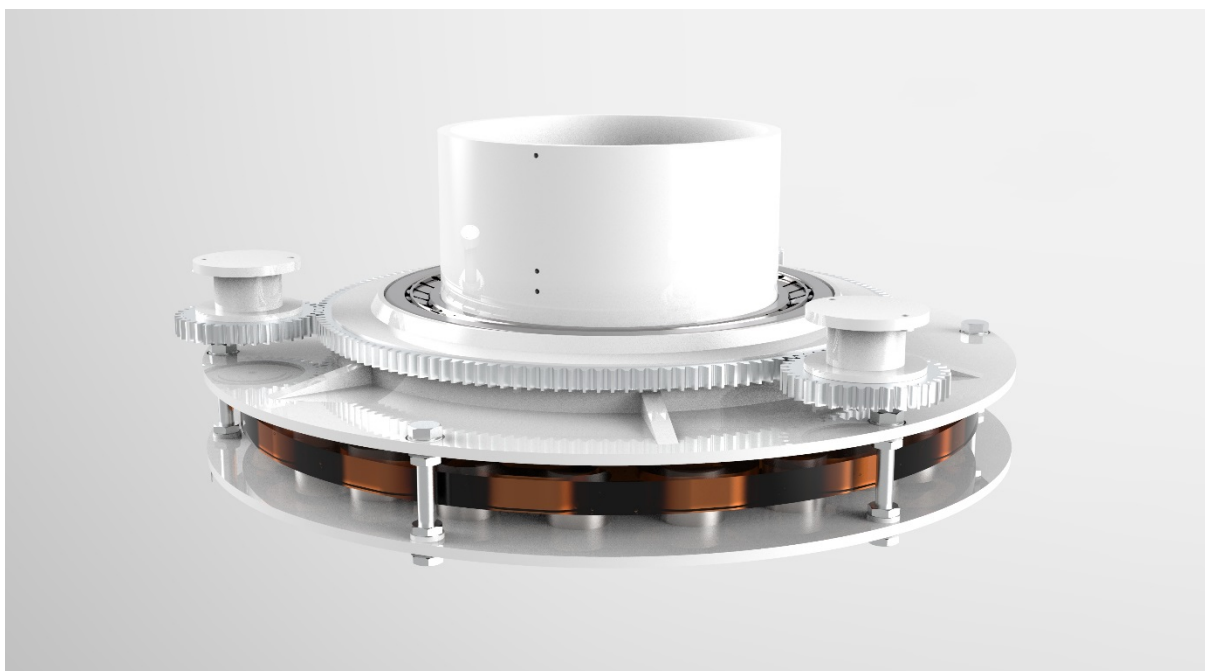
Engranajes planetas, engranaje sol y generador (14.1, 14.2 y 14.3).
